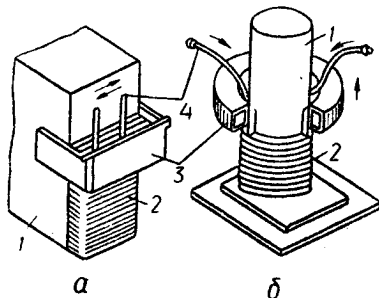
Схема електрошлакового наплавлювання плоскої (а) і циліндричної (б) поверхонь:
